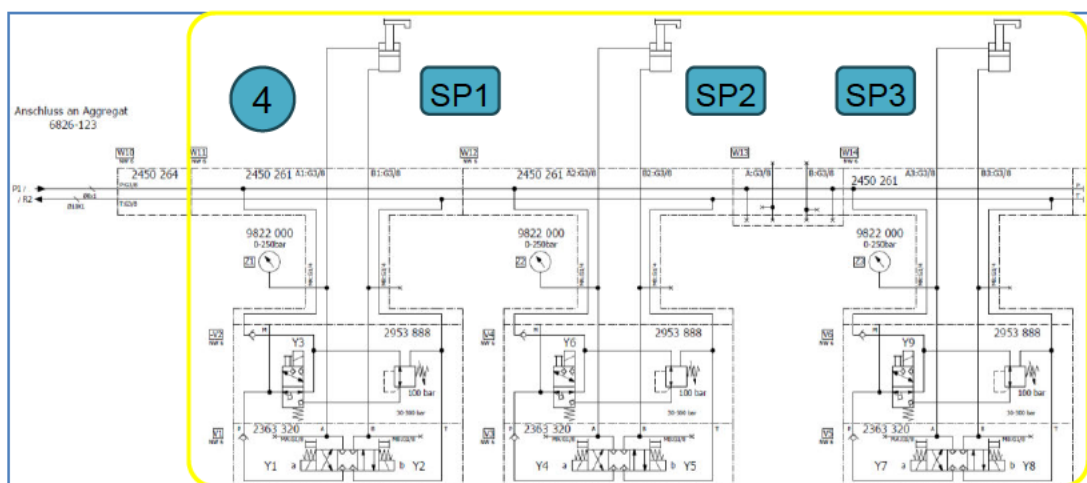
Hydraulikplan - Schwenkspanner 1-3
